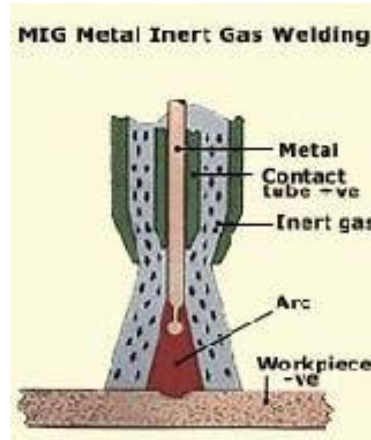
Elementos del arco de soldadura MIG.
